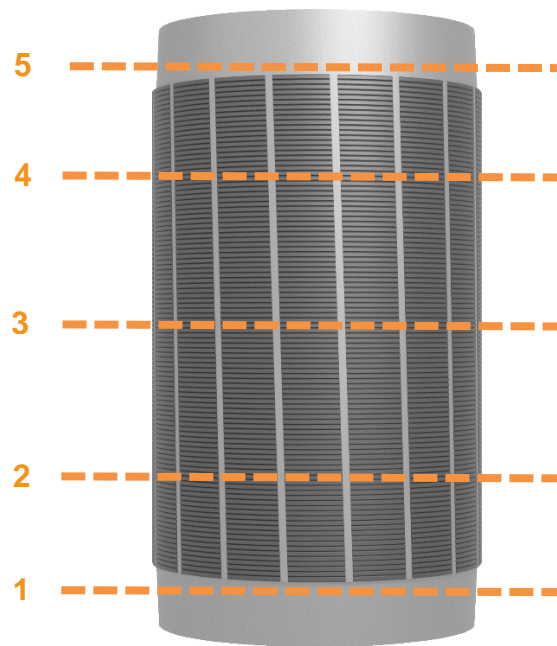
Gesamtansichten der CT-Aufnahmen an einem schwerkraftgegossenen Testrotor
